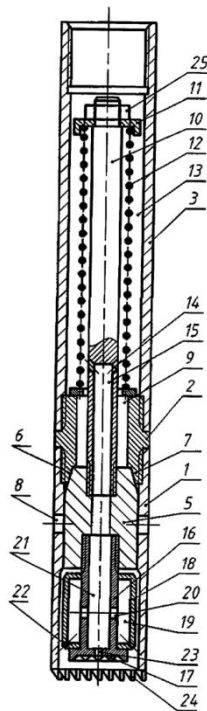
Схема гидроударного устройства 1 – основание гидроударника; 2 – посадочный паз; 3 – переходной элемент; 5 – кольцевой поршень; 6 – конусный паз; 7 – коническая поверхность; 8 – циркуляционные отверстия; 9 – осевой канал; 10 – полый шток; 11 – опорная шайба; 12 – пружинный элемент; 13 – кольцевая щель; 14 – радиальный канал; 15 – осевой канал; 16 – коронка; 17 – зубья; 18 – гидромониторная насадка; 19 – кольцевая камера; 20 – радиальные каналы; 21 – осевой канал; 22 – отверстия; 23 – дроссель; 24 – разрушающие зубья; 25 – крепёжное изделие с резьбовым отверстием
